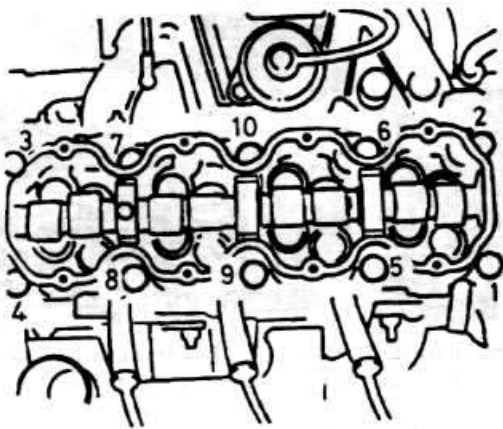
Последовательность ослабления болтов головки блока цилиндров — двигателя с одним распредвалом
